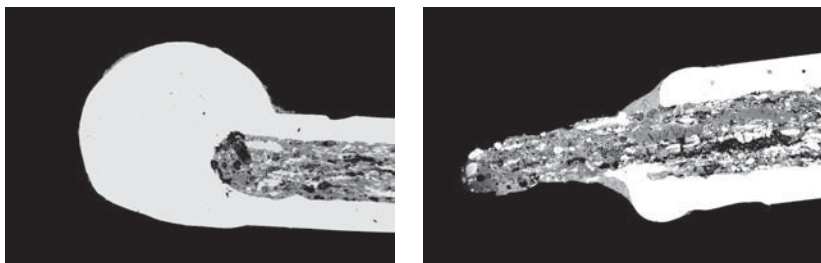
Tropfenbildung beim Schweißen mit Fülldrähten
